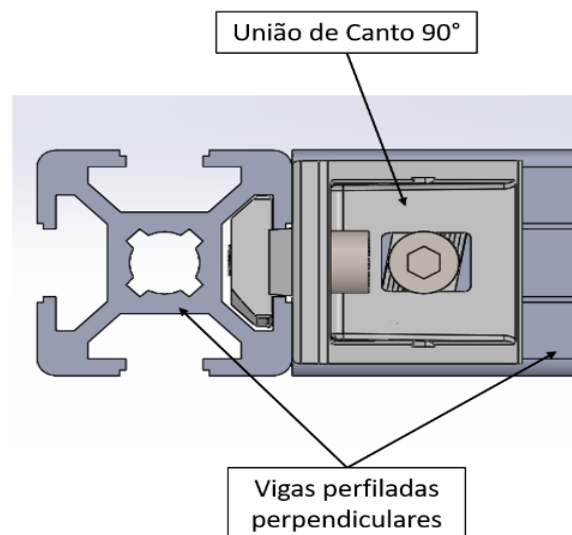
Aparafusamento de uma união de canto ao perfil estrutural
